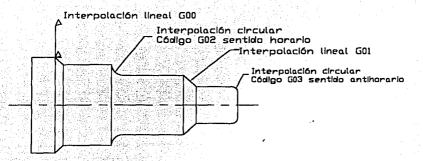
Ciclo de torneado con los códigos G00, G01, G02 y G03
